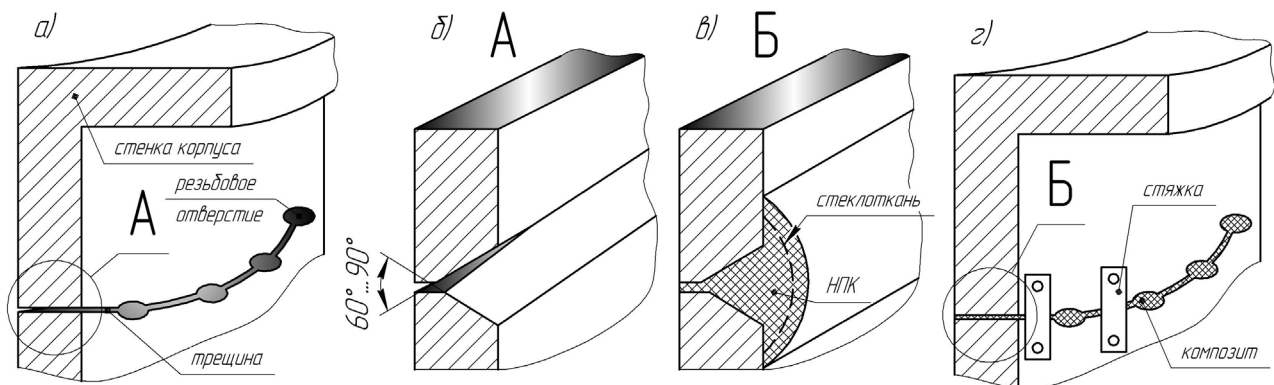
Ремонт стенки корпусной детали: а – сверление по длине и на концах трещины отверстий, нарезание в них резьбы; б – трещина, подготовленная для нанесения НПК; в – заделка трещины, включающая вклеивание в отверстия с применением НПК армирующих резьбовых элементов (шпильки, болты, винты, штифты) и нанесение на трещину НПК, упрочненной стеклотканью; г – установка скоб или стяжек
